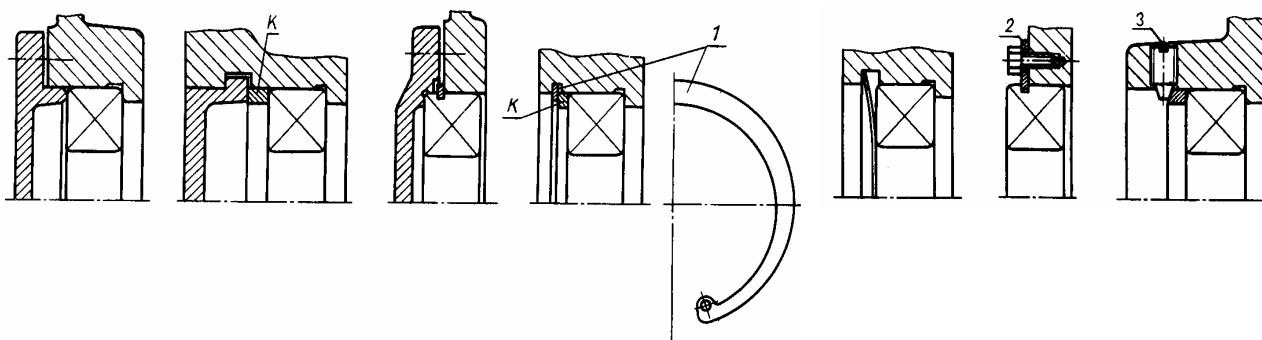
Способы фиксирования наружных колец подшипников в корпусе:
